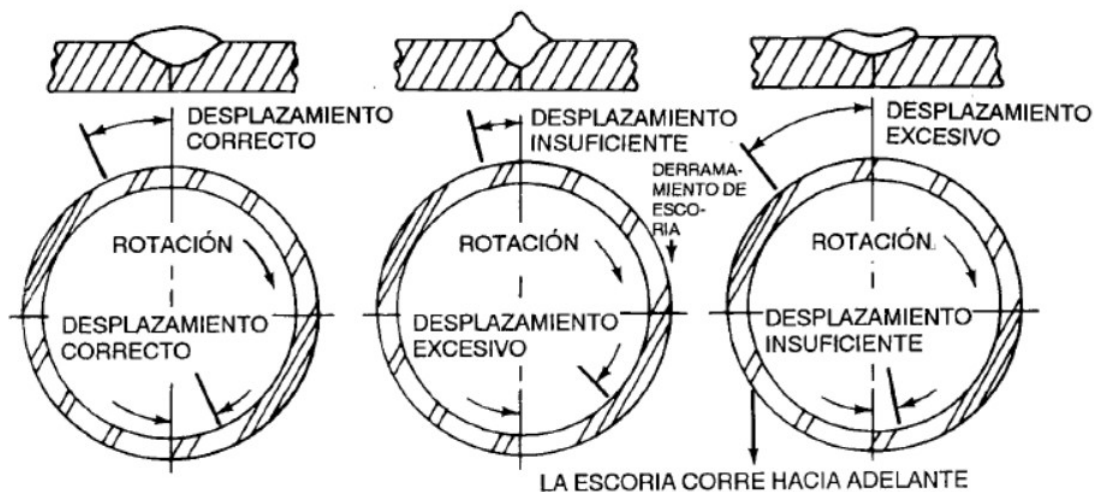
Efecto del desplazamiento del cordón de soldadura en la geometría del cordón de soldadura (4).
